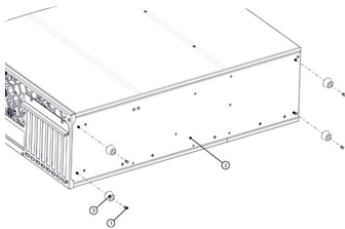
Установка резиновых опор на корпус при вертикальном положении корпуса
